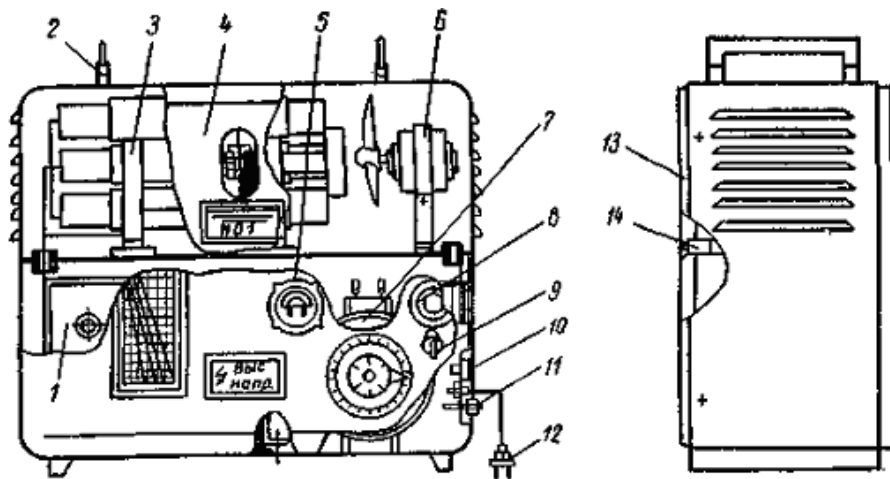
Пересувний озонатор: 1 – високовольний трансформатор; 2 – ручки; 3 – камера; 4 – корпус; 5 – вольтметр; 6 – вентилятор; 7 – варіатор напруги; 8 – сигнальна лампа; 9 – вимикач; 10 – перемикач напруги; 11 – запобіжник; 12 – штепсельна вилка; 13 – знімна кришка; 14 – блок-контакт
